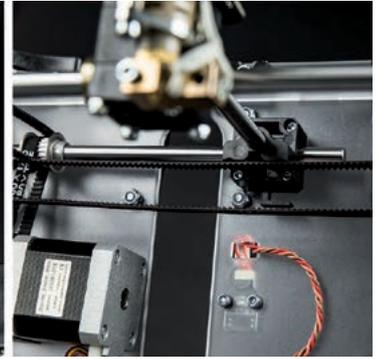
Ensamblado del cabezal de impresión de único extrusor.
